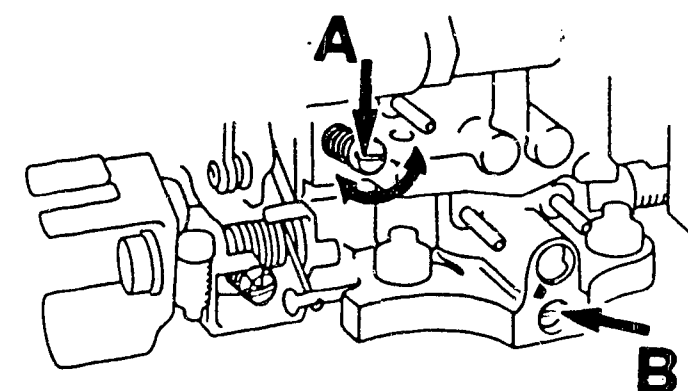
Vergaser auf dem Motor 21R-C: Einstellschrauben für Leerlaufgemisch (A) und Leerlaufdrehzahl (B).
